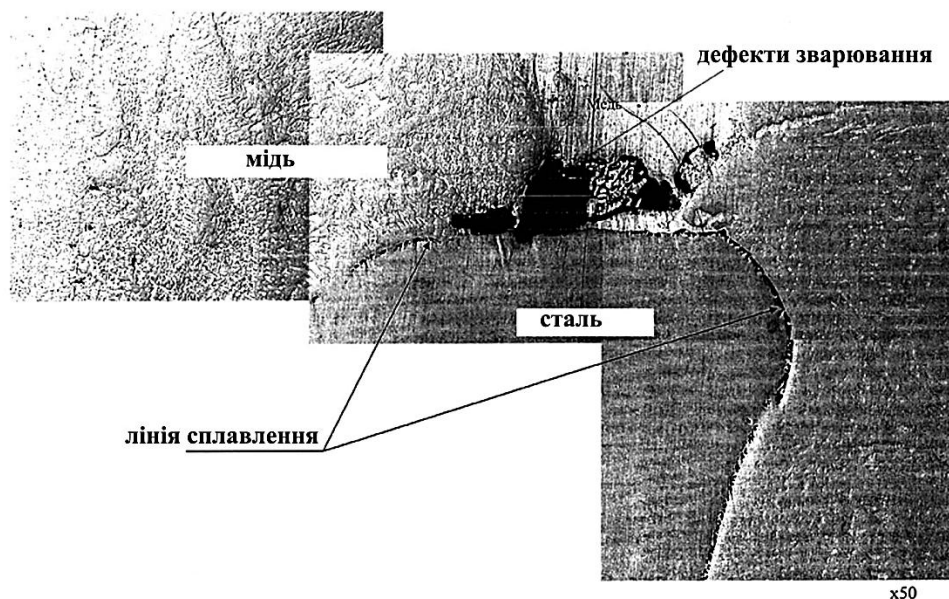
Дефекти зварного з'єднання міді зі сталлю
